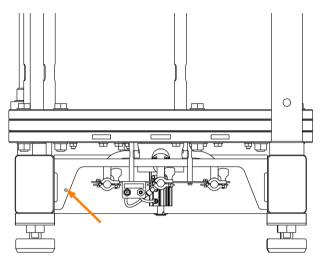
Punto di collegamento sulla struttura della colonna per il cavo di messa a terra di protezione.
